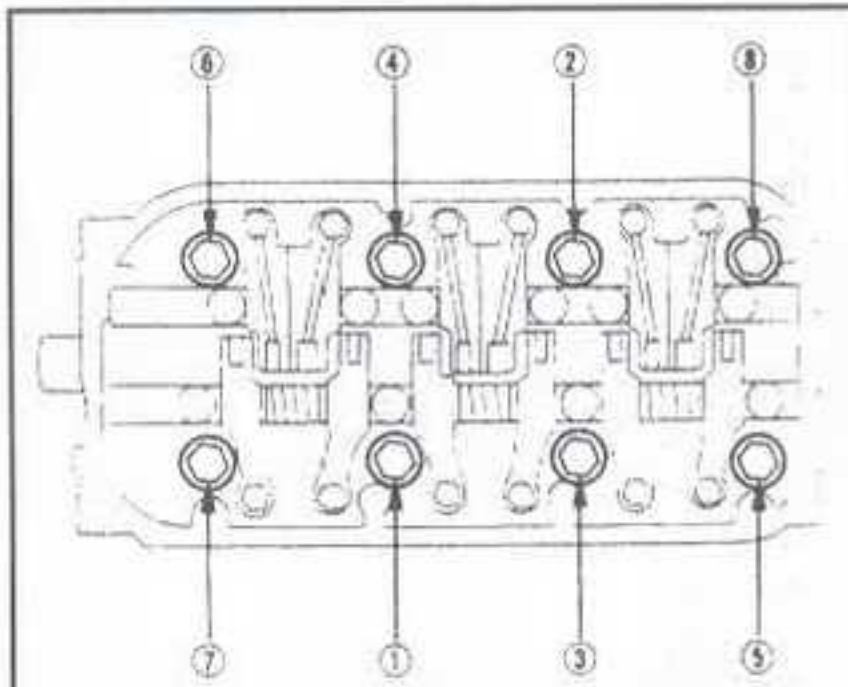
Порядок затяжки болтов головки цилиндров - двигателя V6 моделей Odyssey
